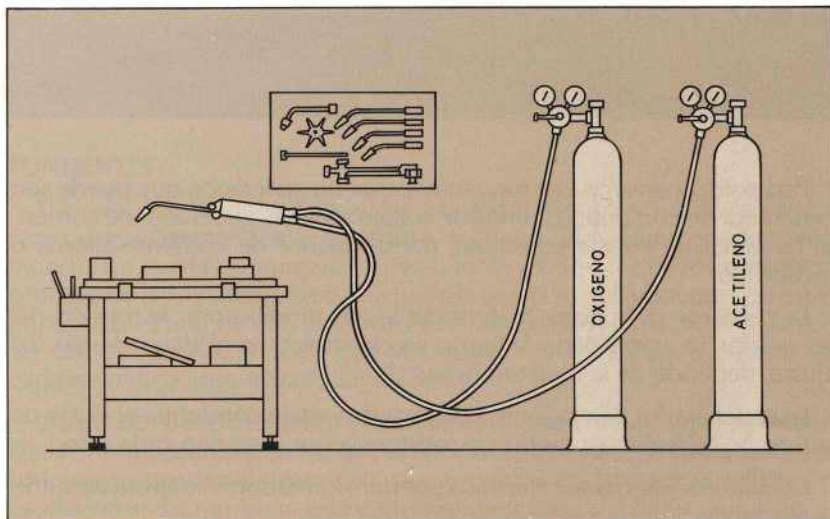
Esquema de los principales elementos para la soldadura oxiacetilénica.
